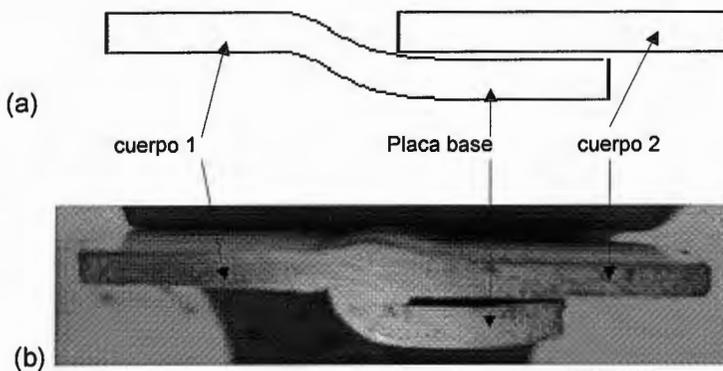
(a) Pestaña o hendidura que sirve como placa de respaldo a las soldaduras de los cuerpos del envase (b) Fotografía de la unión soldada. Se puede apreciar como la placa de respaldo se convierte en parte de la unión
